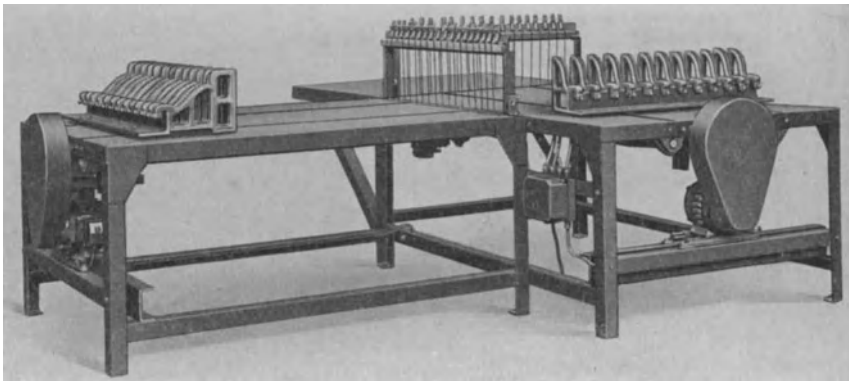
Kombinierte Zerschneidemaschine für große Seifenplatten (Weber & Seeländer, Helmstedt).
